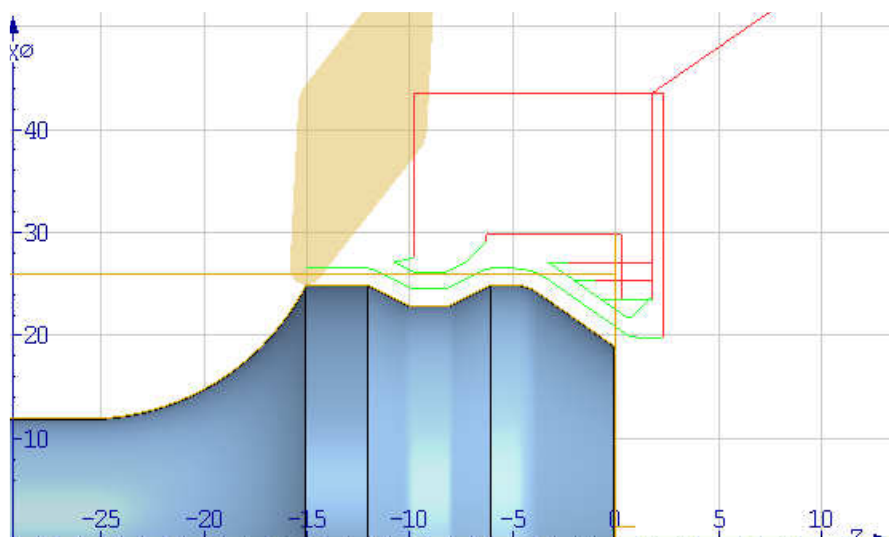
Vyhrubovanie tvarového drieku veže
